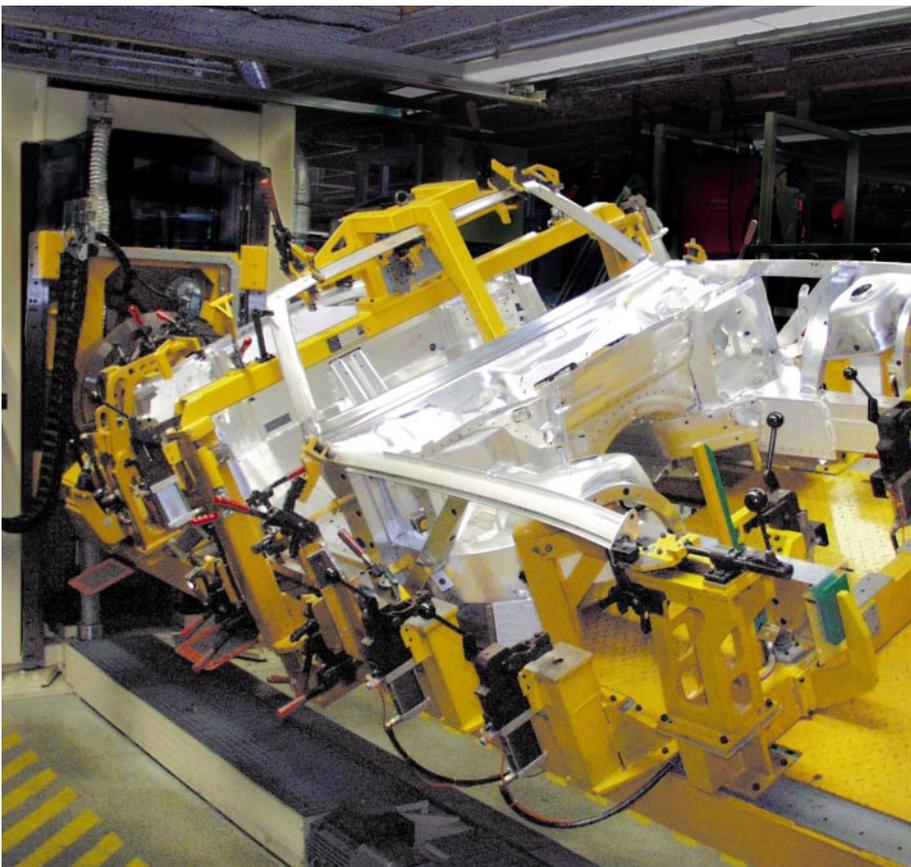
Schweißvorrichtung Drehtrommel
